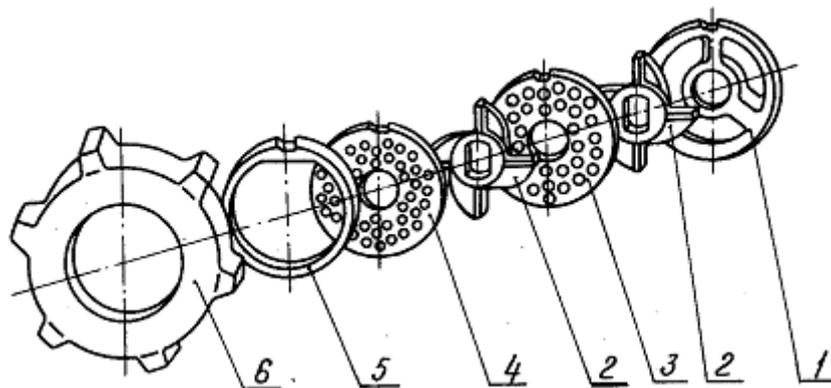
Схема основного ножевого набора мясорубки
